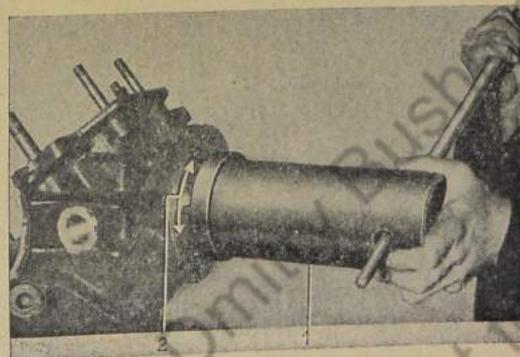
Einstellbuchse durch leichte Hammerschläge einschlagen, bis das Gewinde gefaßt hat
